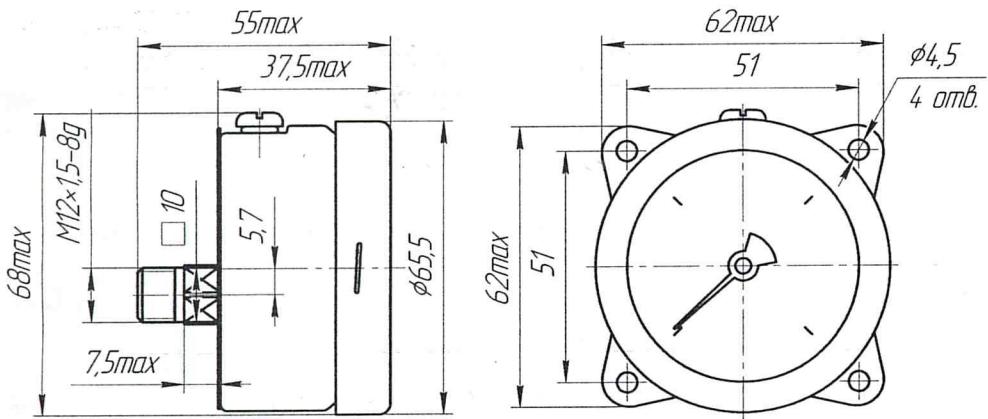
Габаритные и присоединительные размеры приборов с осевым расположением штуцера с фланцем
